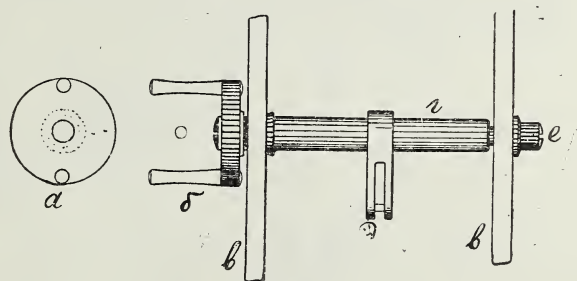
Деталь верхней механики а—вилочка an face, б—вилочка сбоку, вв — металлические стенки, г—валик, д—передаточный рычажок, е—наружный винтик.
